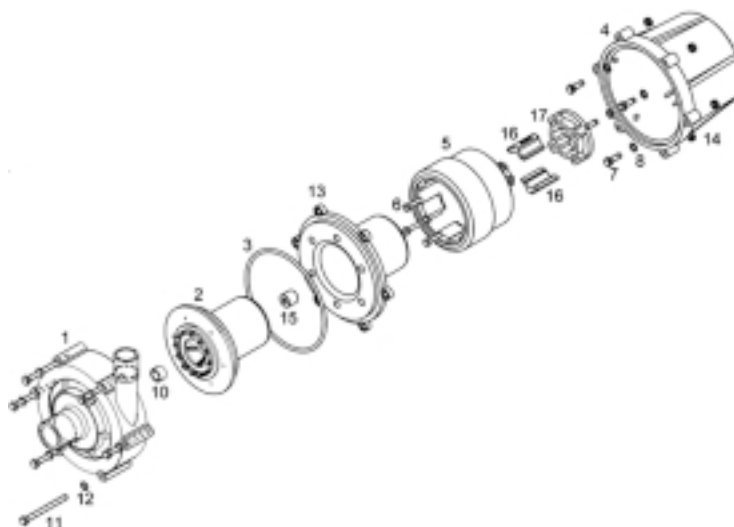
Exploded drawing vonTAINÉ AM 300 / AM 400
